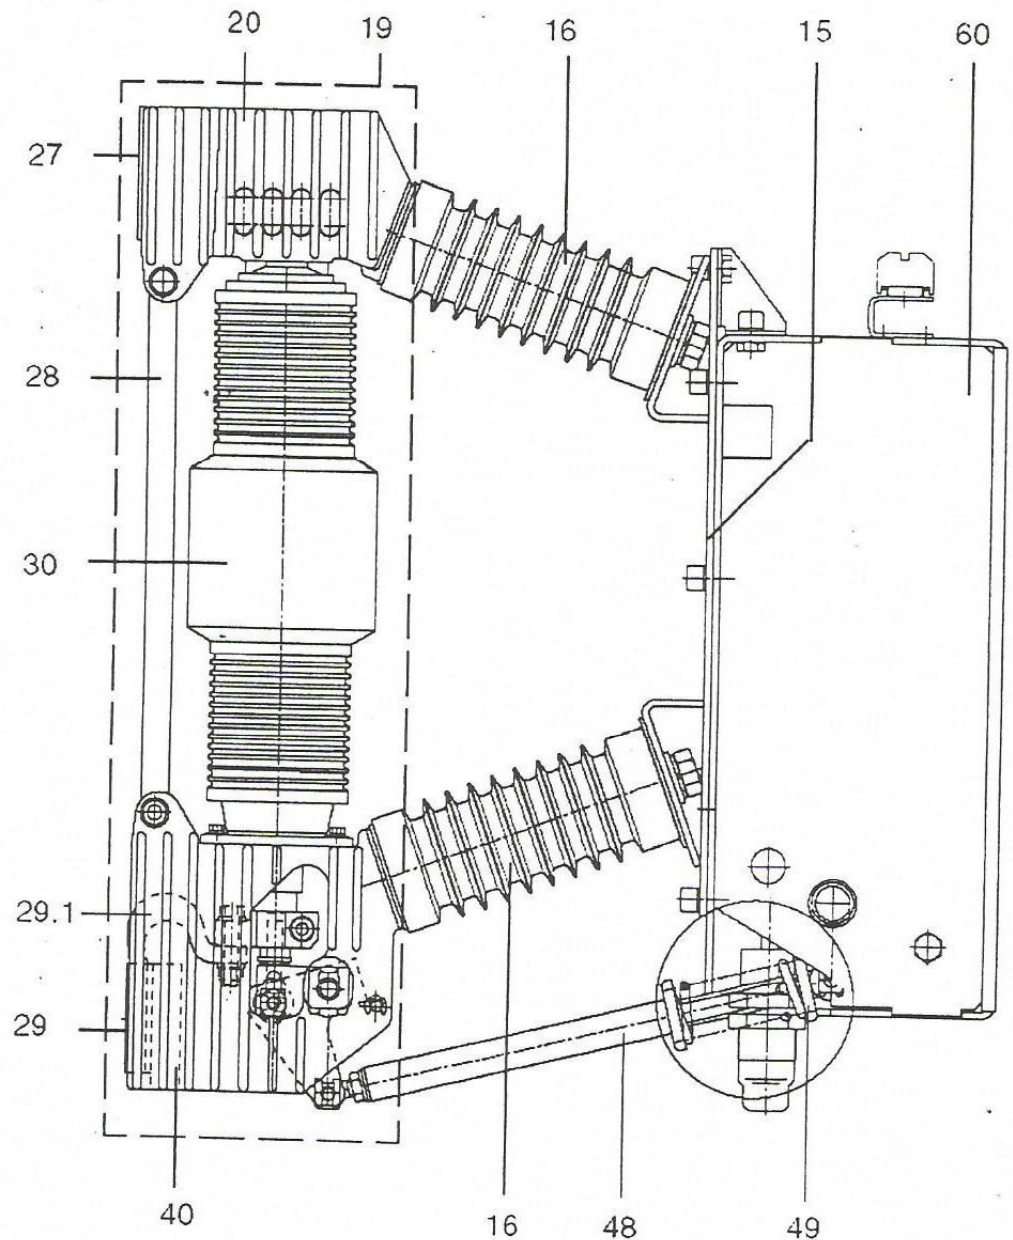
Общий вид полюса выключателя ЗАН-27.5
